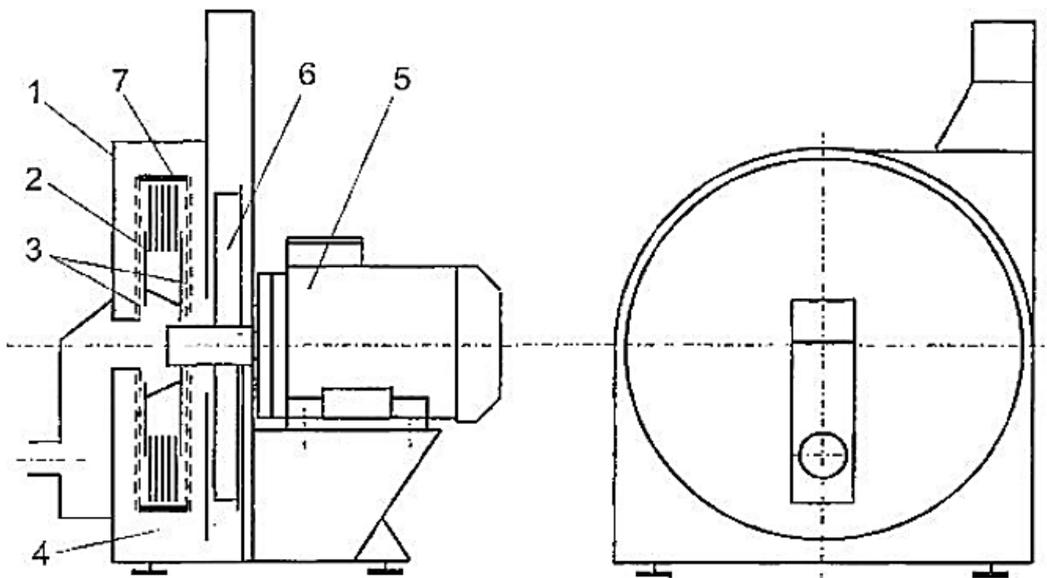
Молоткова дробарка з торцевими решетами: 1 – корпус; 2 – молотковий ротор; 3 – сепаруючі решета; 4 – осаджуюча камера; 5 – електродвигун; 6 – крильчатка вентилятора; 7 – дека
